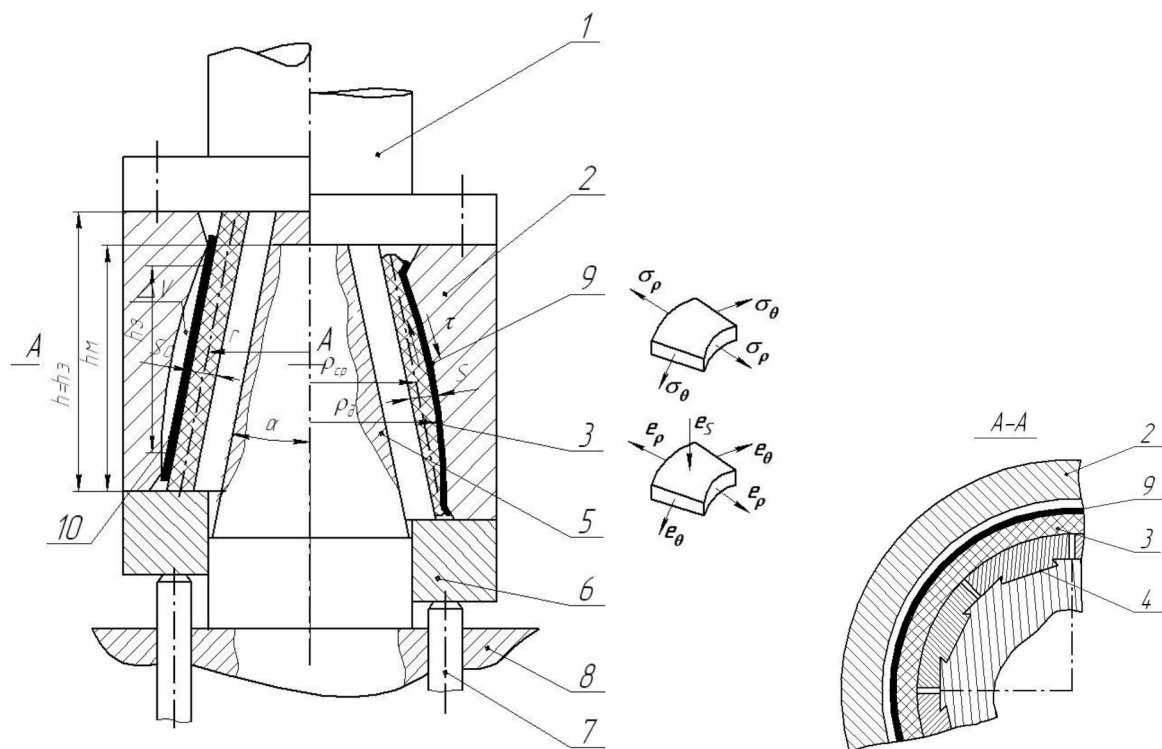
Устройство для формообразования тонкостенных осесимметричных деталей усеченной сужающейся формы
